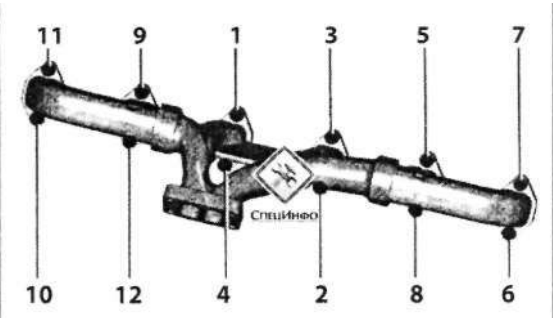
Порядок затяжки болтов крепления выпускного коллектора.
